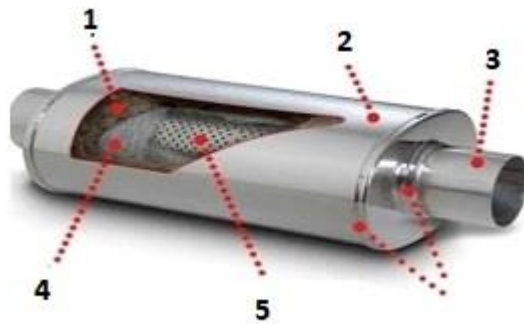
Глушник: 1 – звукопоглинаючий матеріал; 2 – корпус; 3 – випускний патрубок; 4 – сталева сітка; 5 – перфорована труба; 6 – зварні шви
